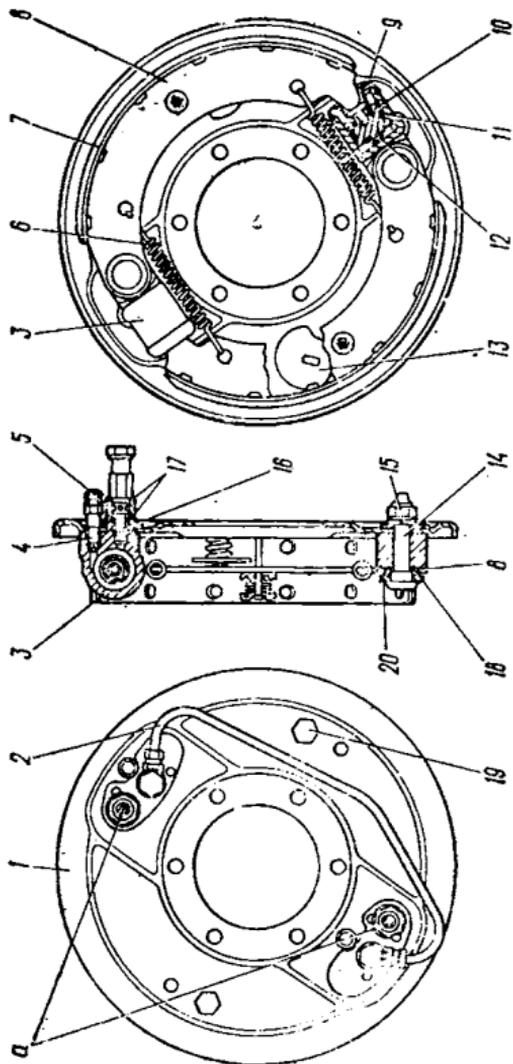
Тормоз переднего колеса автомобиля УАЗ-469Б:
